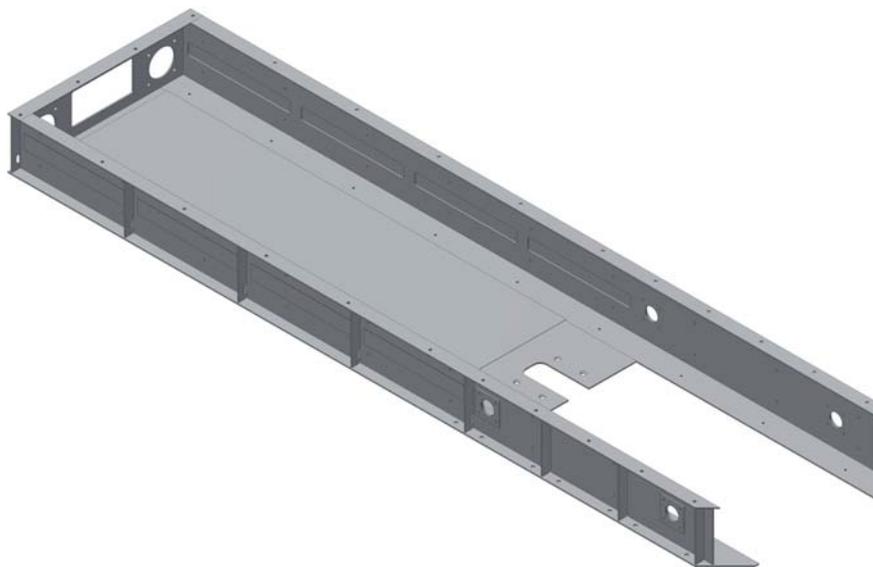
Tunnel-Schweißbaugruppe
